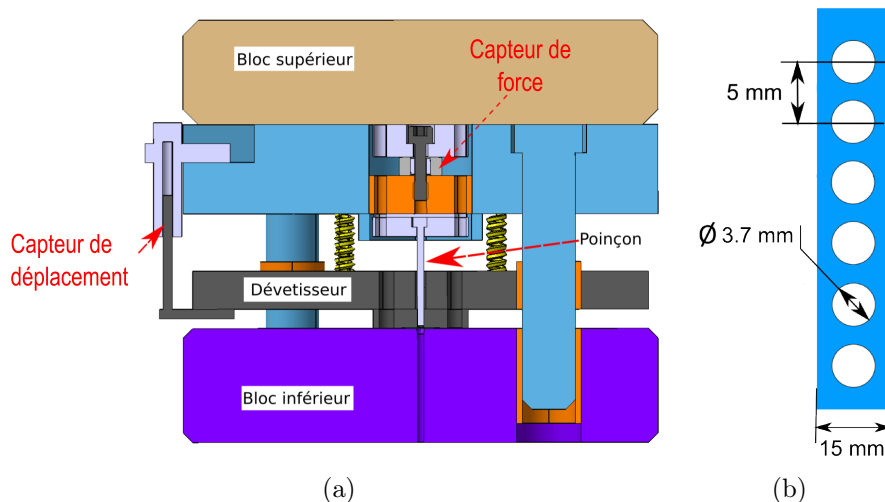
(a) Vue en coupe de l'outil de découpe utilisé pour réaliser les essais de découpage, (b) Schéma de la tôle découpée.
